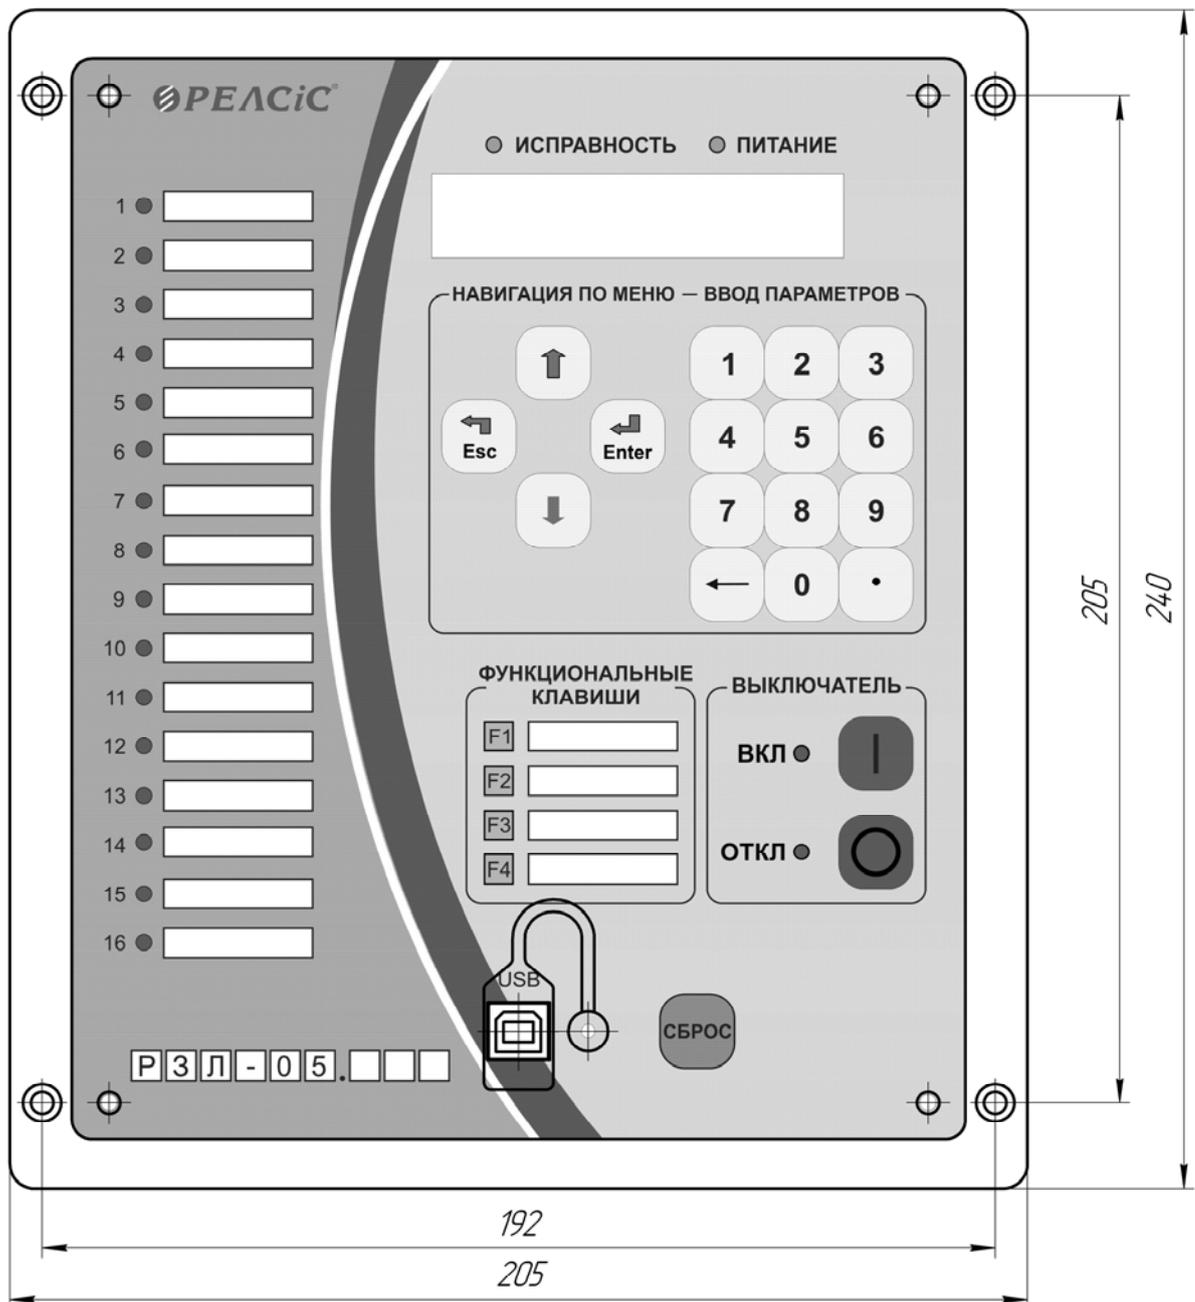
Габаритные размеры и установочные размеры и внешний вид передней панели устройства РЗЛ-05.Ф1(2) Л01
